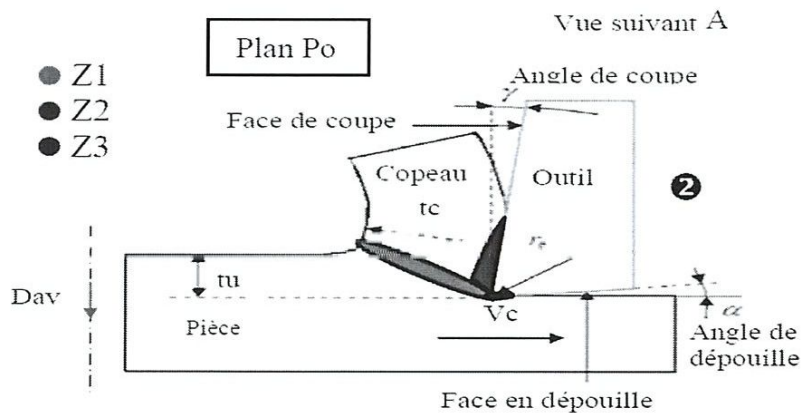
Formation du copeau en coupe orthogonale[A03].
